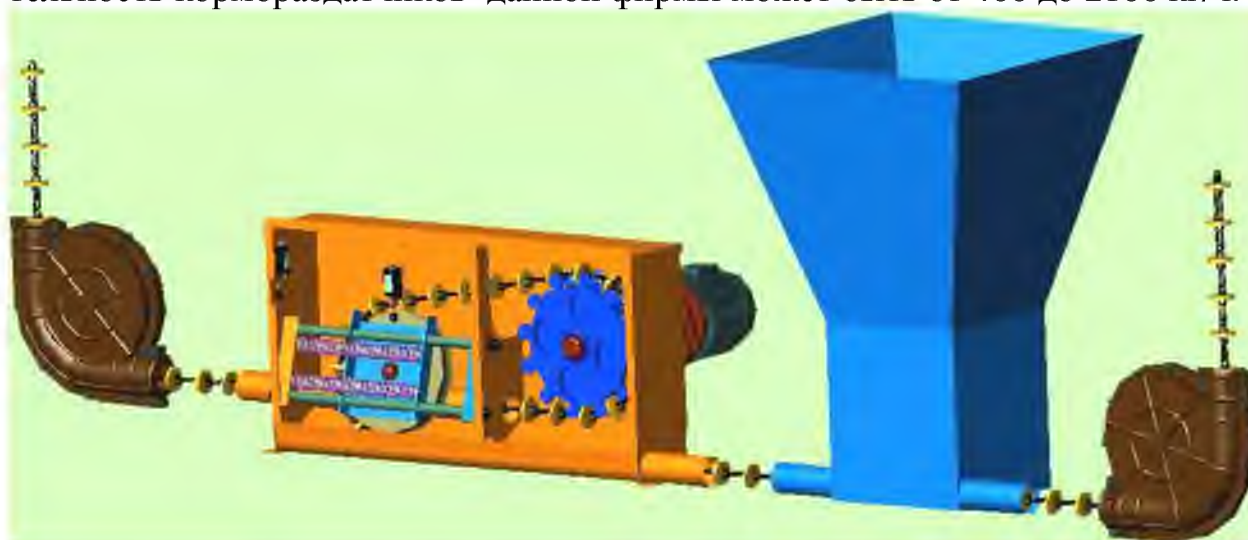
Конструктивный вид канатного транспортеры для раздачи корма
